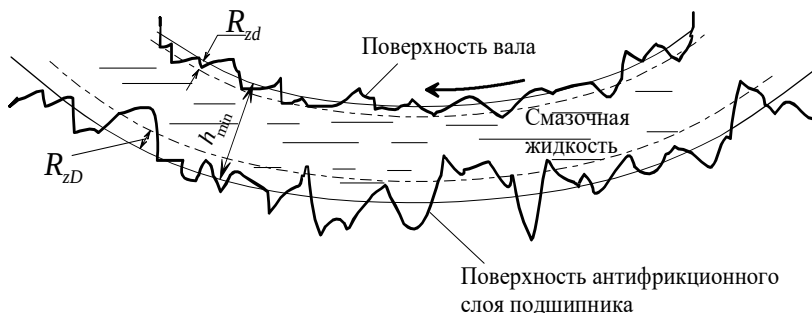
Схема для расчета минимально допустимой толщины смазочного слоя для обеспечения режима жидкостной смазки
